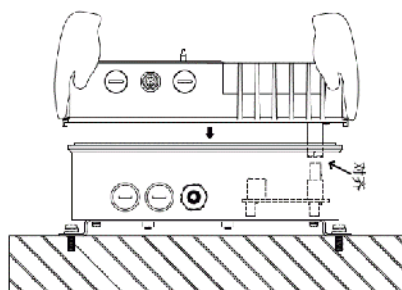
Установка средней части корпуса обратно на соединительную коробку
